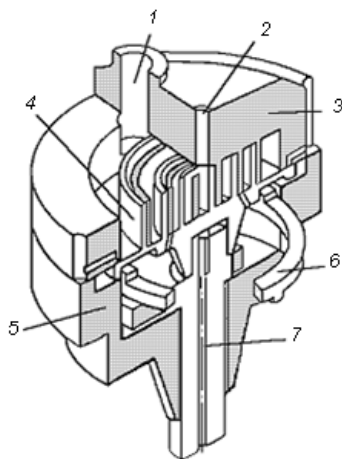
СПК в разрезе: 1 — патрубок всасывания; 2 — отверстие нагнетания; 3 — неподвижная спираль; 4 — подвижная спираль; 5 — корпус СПК; 6 — диск противоповоротного устройства; 7 — приводной вал
